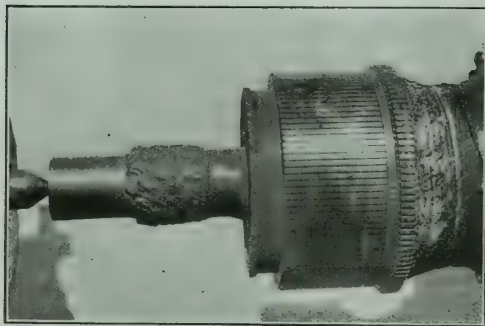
SOLDADURA EN ESPIRAL SOBRE MUÑÓN DE UN EJE DE INDUCIDO
